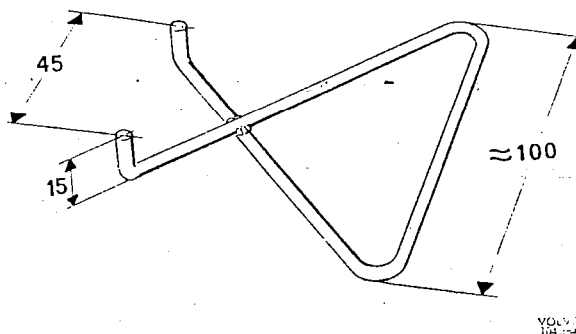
47 Ausziehhaken für Kabelbaumstecker
